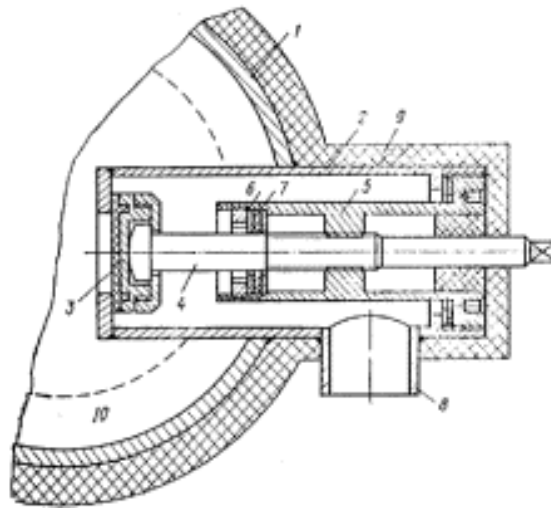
Конструкция выпуска воды при оледенении трубопровода на 50 %
